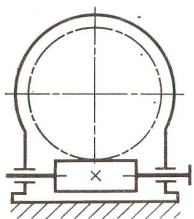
Червячный редуктор с нижним расположением червяка
